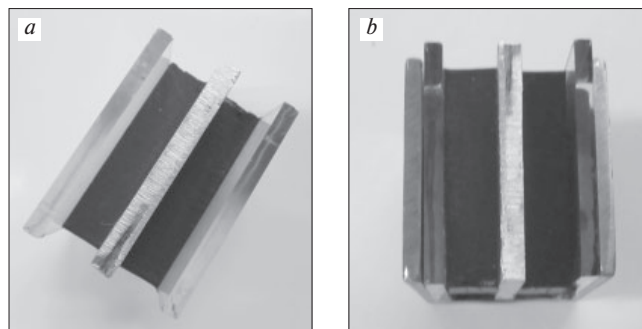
Образец-шов стекло–алюминий–стекло для проведения испытаний на сдвиг: a – образец-шов; b – образец-шов установлен в приспособление для испытаний на сдвиг
